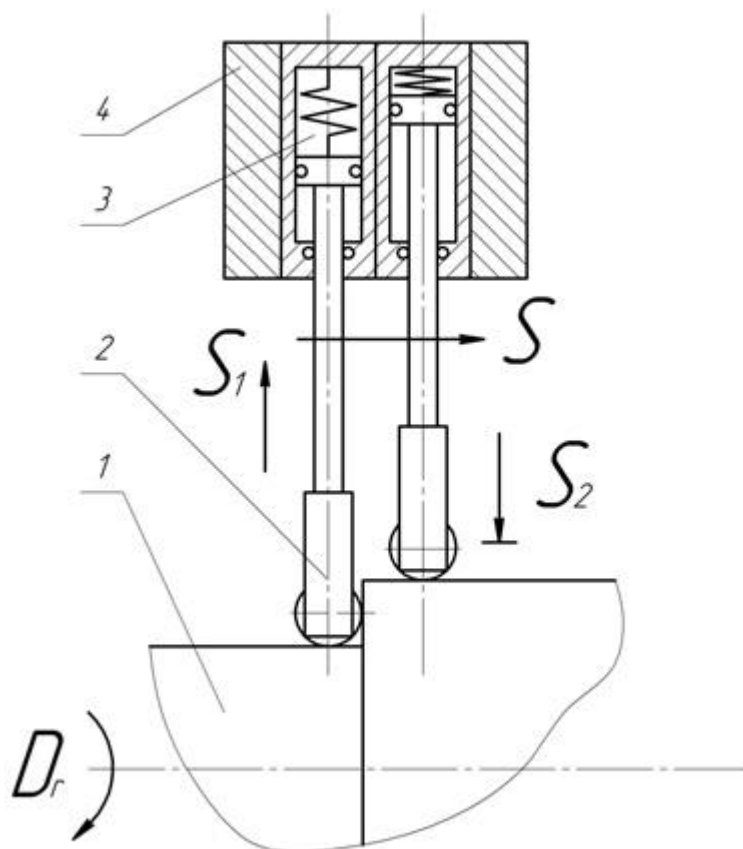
Расположение стержней подвижного люнета: 1 – заготовка, 2 – подвижный стержень люнета, 3 – гидrocилиндр, 4 – корпус люнета.
